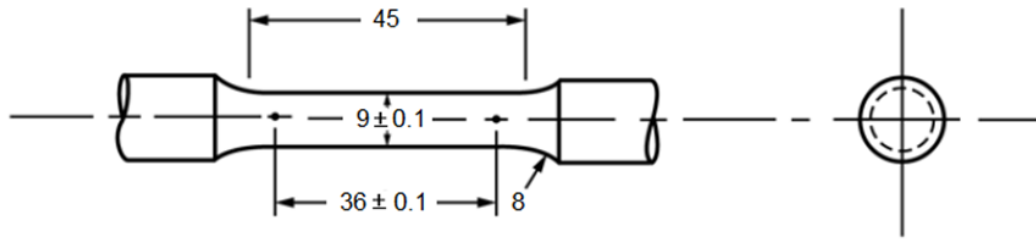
Geometría y dimensiones en [mm] de cada probeta cilíndrica, según ASTM E8 – 04.
